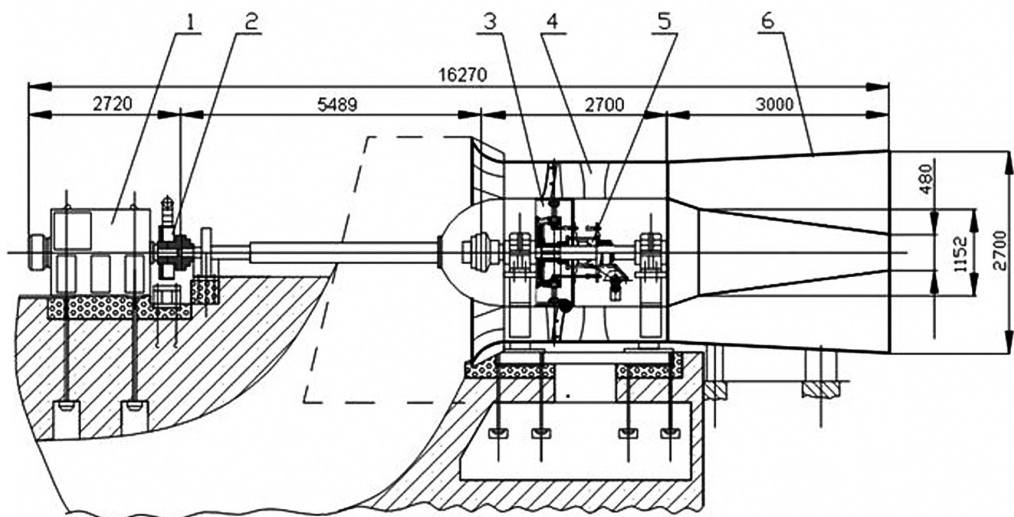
Схема вентиляторного агрегата серии ВО: 1 – синхронный электродвигатель 630 кВт, 750 об/мин, 6,0 кВ; 2 – электромагнитный тормоз; 3 – рабочее колесо с поворотными на ходу сдвоенными листовыми лопатками; 4 – неповоротные лопатки спрямляющего аппарата; 5 – механизм одновременного поворота лопаток рабочего колеса; 6 – диффузор
